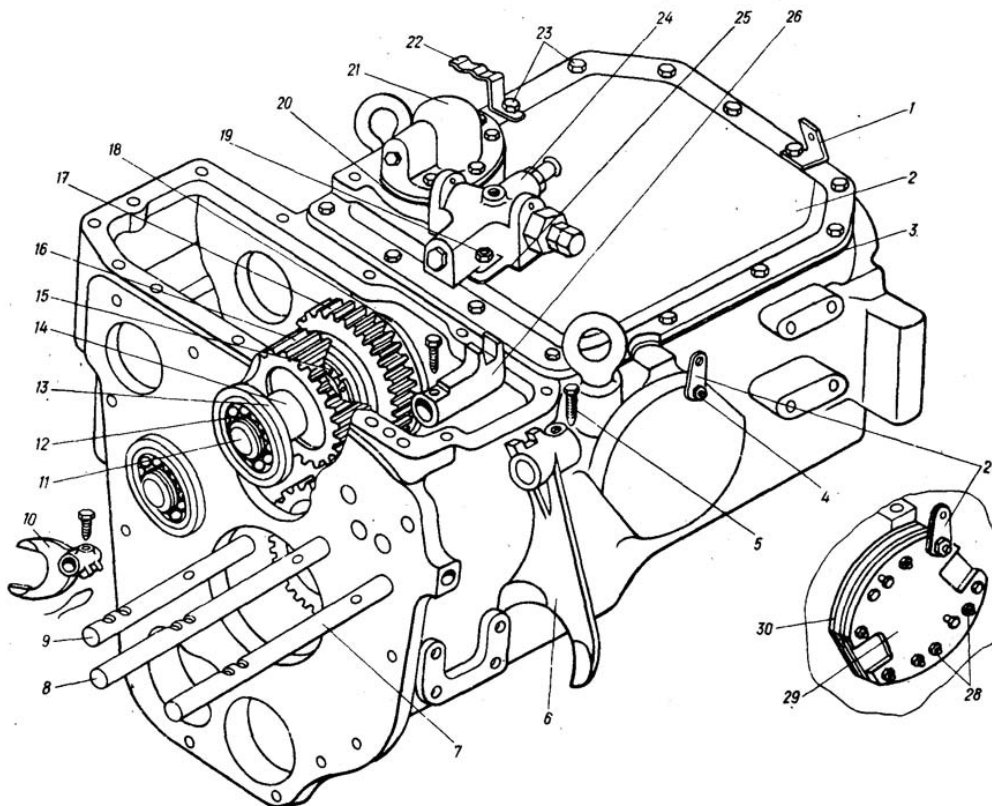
Установка крышки, распределителя, зубчатых колес заднего хода:
